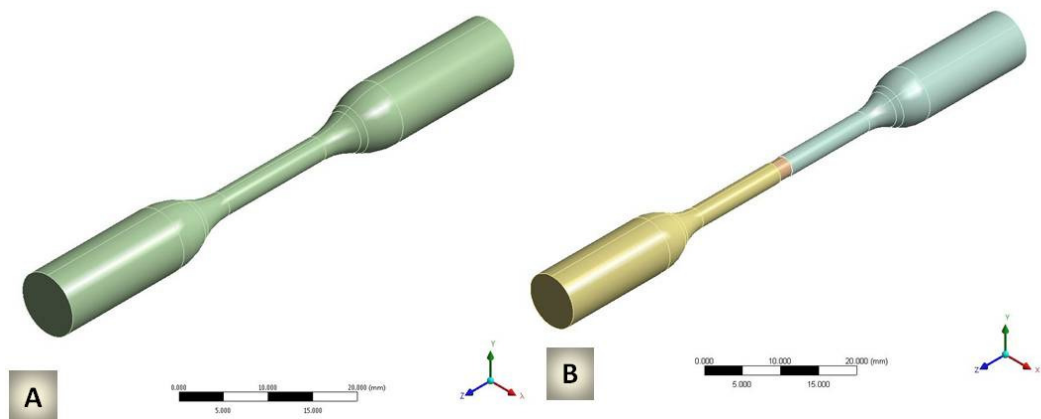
a) Corpo de prova intacto (grupo controle) e b) Corpo de prova soldado
